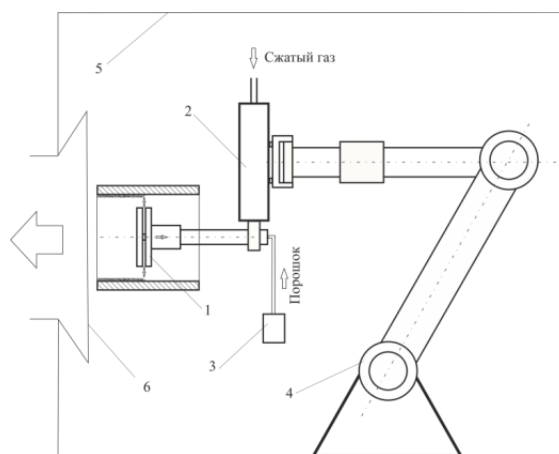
Схема устройства газодинамического нанесения покрытий на внутренние цилиндрические поверхности.
